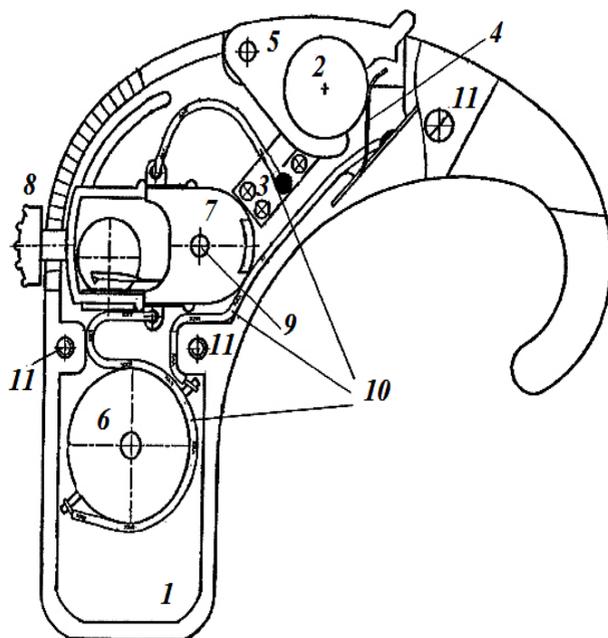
Устройство для предупреждения от засыпания водителя ТССН: 1 – корпус серповидной формы; 2 – источник питания; 3 – выключатель; 4 – контакт; 5 – держателем; 6 – генератор звукового сигнала; 7 – датчик угла наклона; 8 – рукоятка; 9 – поворотная ось; 10 – провод; 11 – винт
